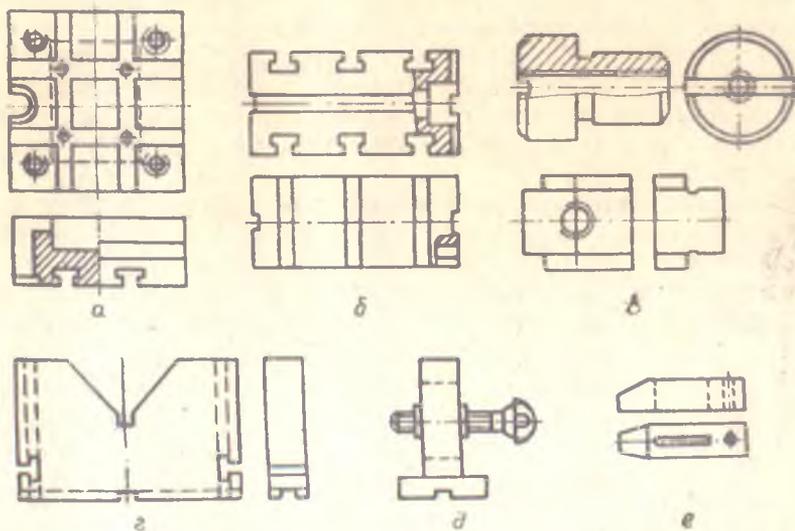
Некоторые детали групп элементов УСП: а — базовые; б — корпусные; в — установочные; г — направляющие; д, е — прижимные
